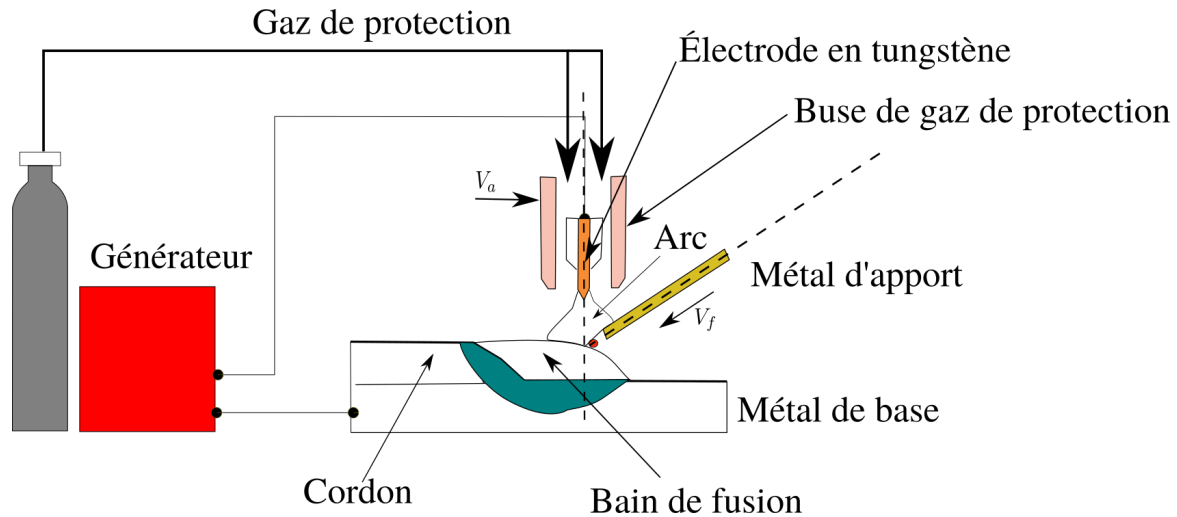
Principe du procédé de soudage TIG.
